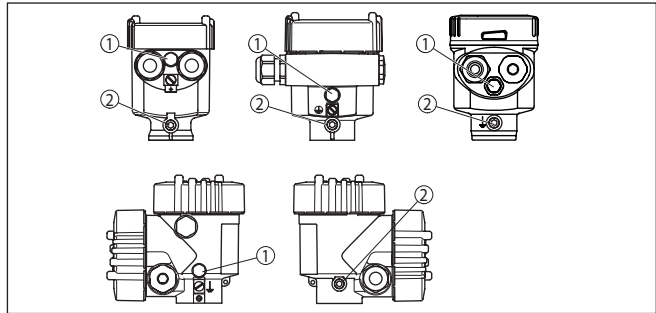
Положение фильтрующего элемента в однокамерном и двухкамерном корпусе
